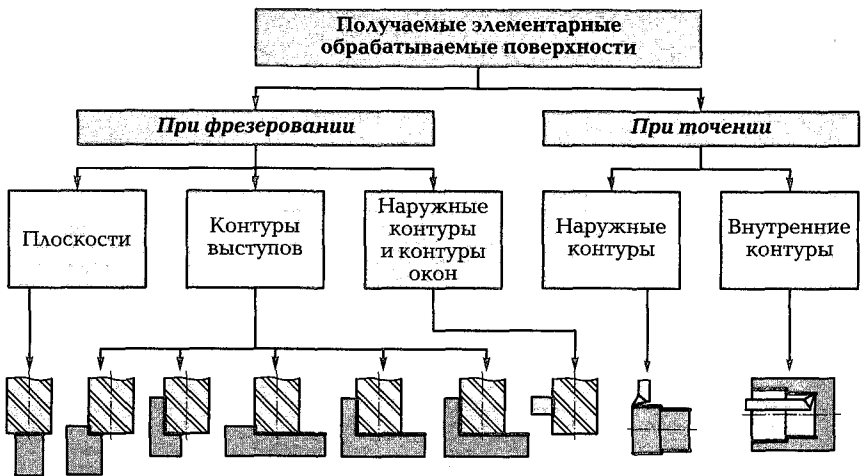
Виды элементарных обрабатываемых поверхностей при фрезеровании и точении
